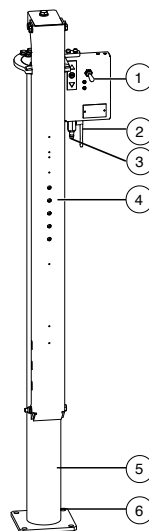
Vista traseira de um elevador de uma coluna sobre um suporte ou chasis
